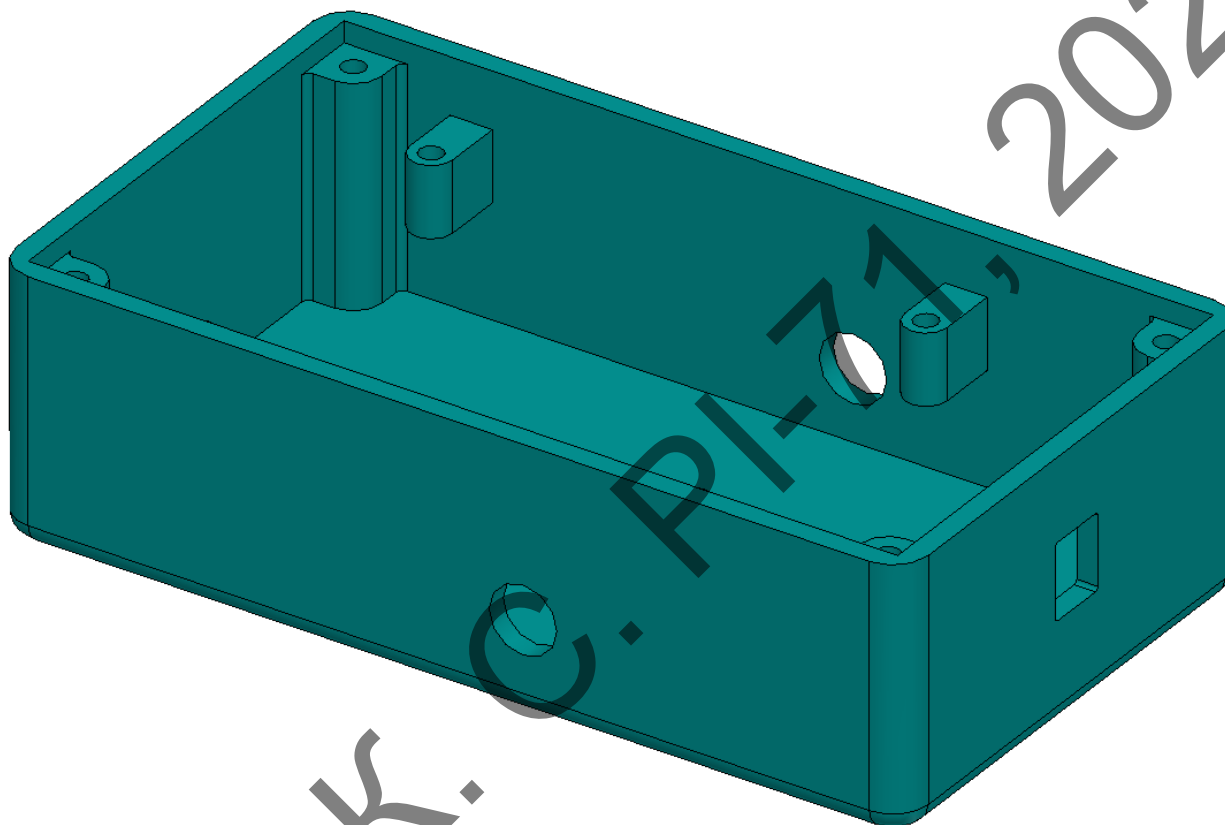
Вигляд знизу основної частини корпусу
